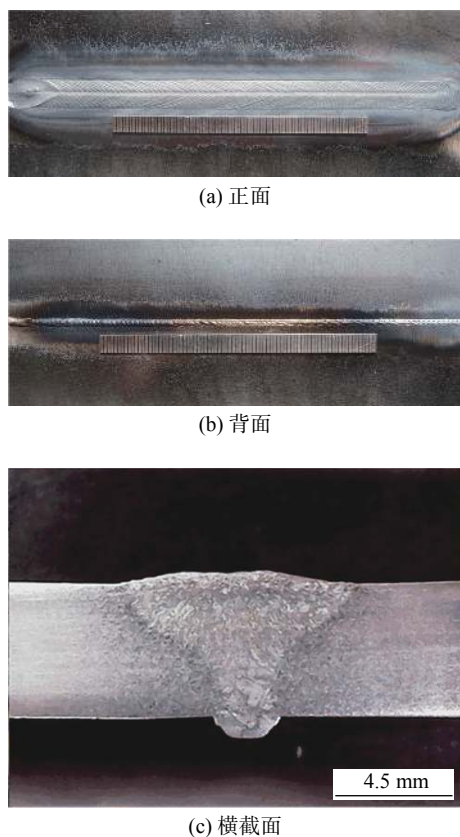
P-T 焊缝正、背面成形及横截面宏观形貌
